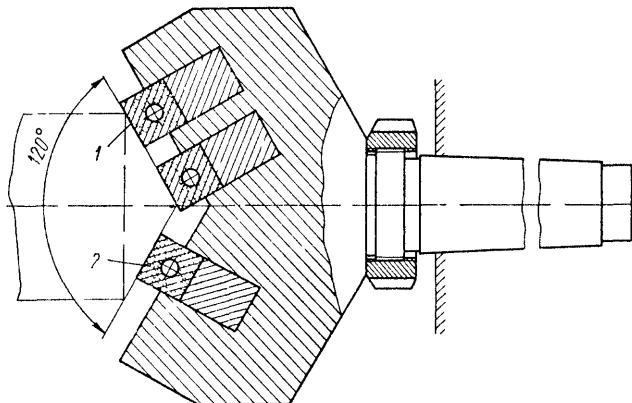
Резцовый блок для обработки конических торцов (угол 120°)
